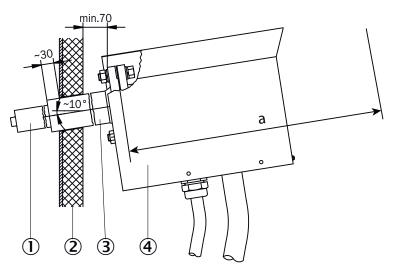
Requisiti di installazione per la flangia di testa a saldare
